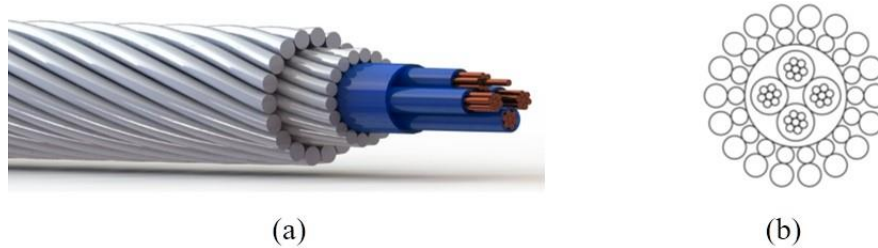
Construcción del cable 4H18RPP. (a) Modelo tridimensional. (b) Corte transversal.
